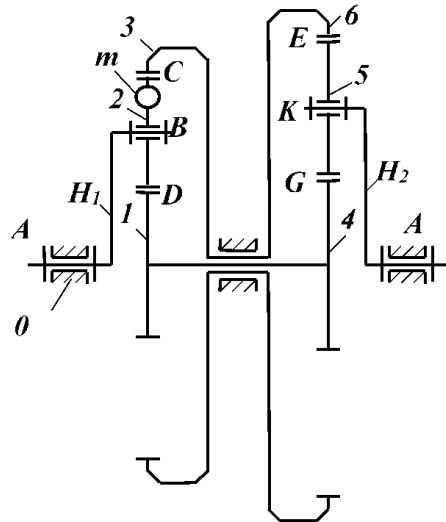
Зубчатый адаптивный вибрационный механизм
